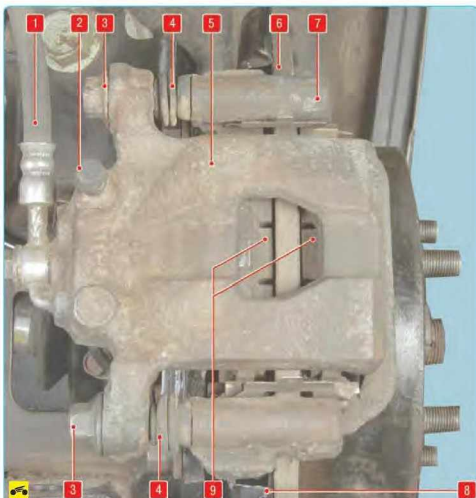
Тормозной механизм заднего колеса: 1 – тормозной шланг; 2 – клапан выпуска воздуха; 3 – направляющие пальцы суппорта; 4 – пыльник направляющего пальца; 5 – суппорт тормозного механизма; 6 – тормозной диск; 7 – направляющая колодок; 8 – шит тормозного механизма; 9 – тормозные колодки
